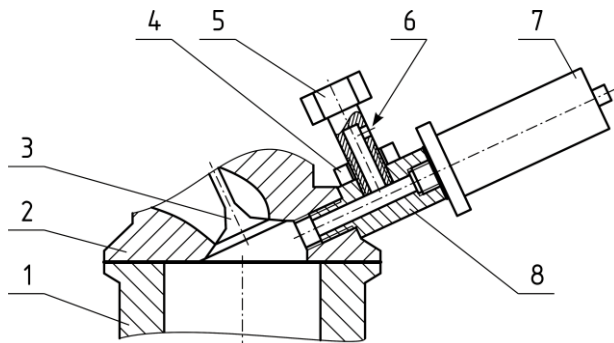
Схема для имитации негерметичности камеры сгорания: 1 – блок цилиндров; 2 – головка блока цилиндров; 3 – клапан; 4 – гайка; 5 – болт; 6 – калибровочное отверстие; 7 – датчик давления; 8 – переходник
